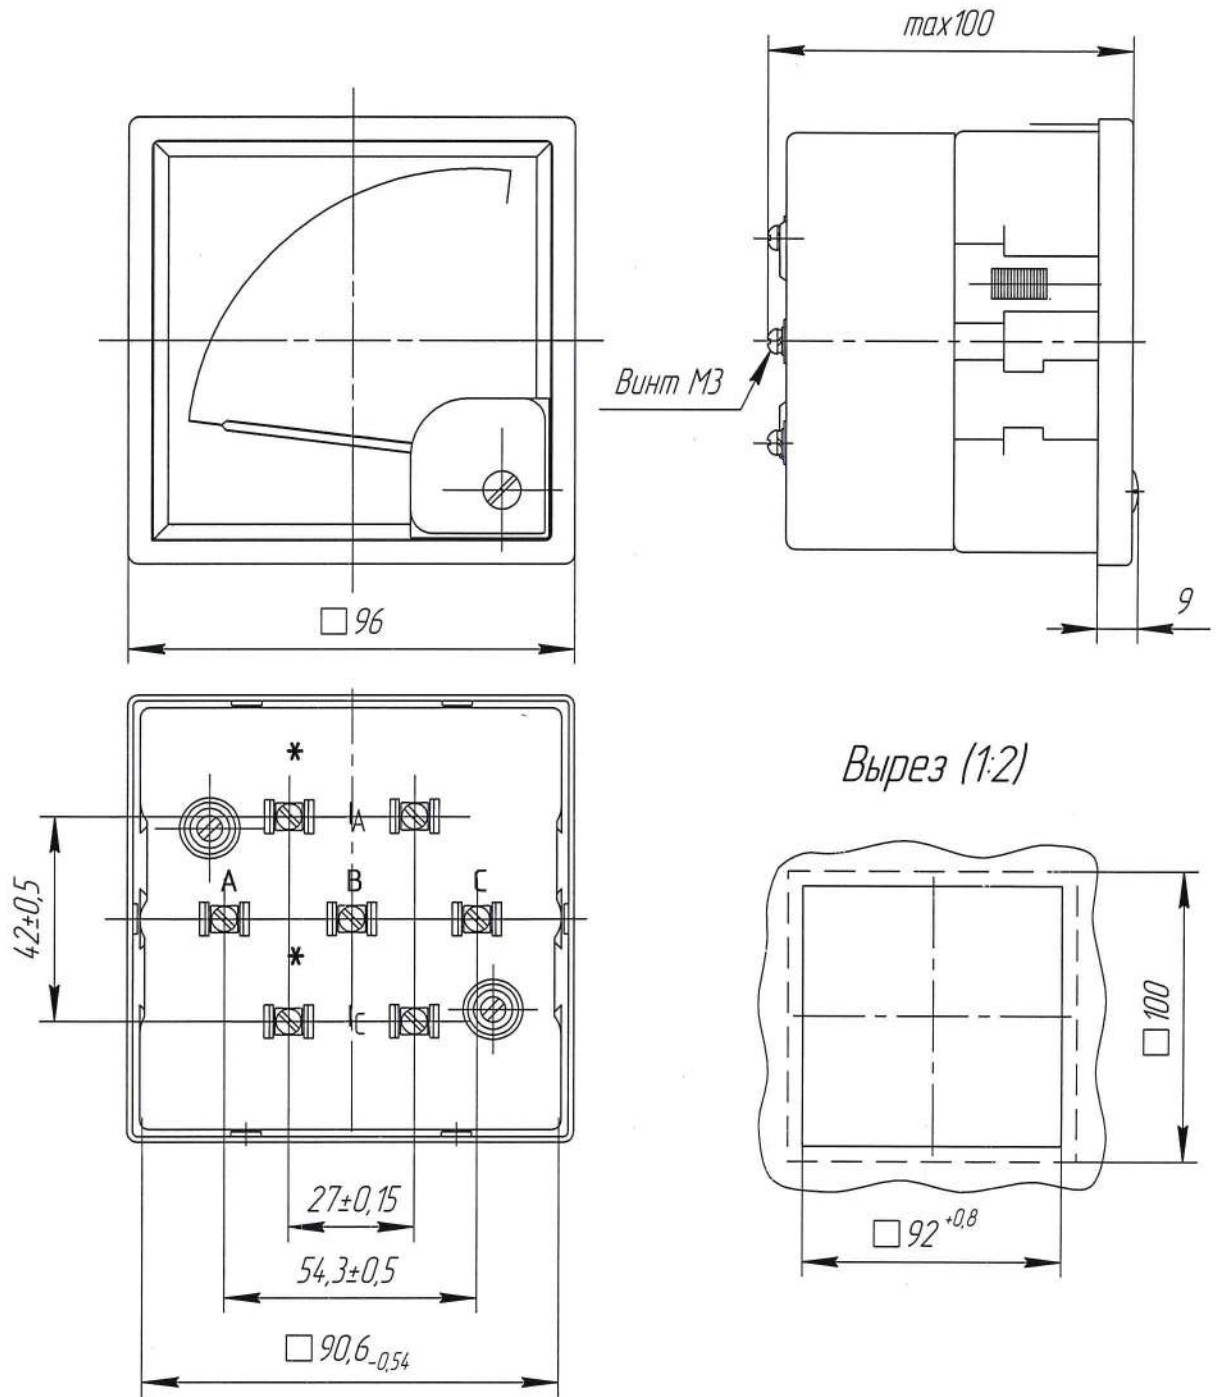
Габаритные размеры и вырез в щите для крепления
